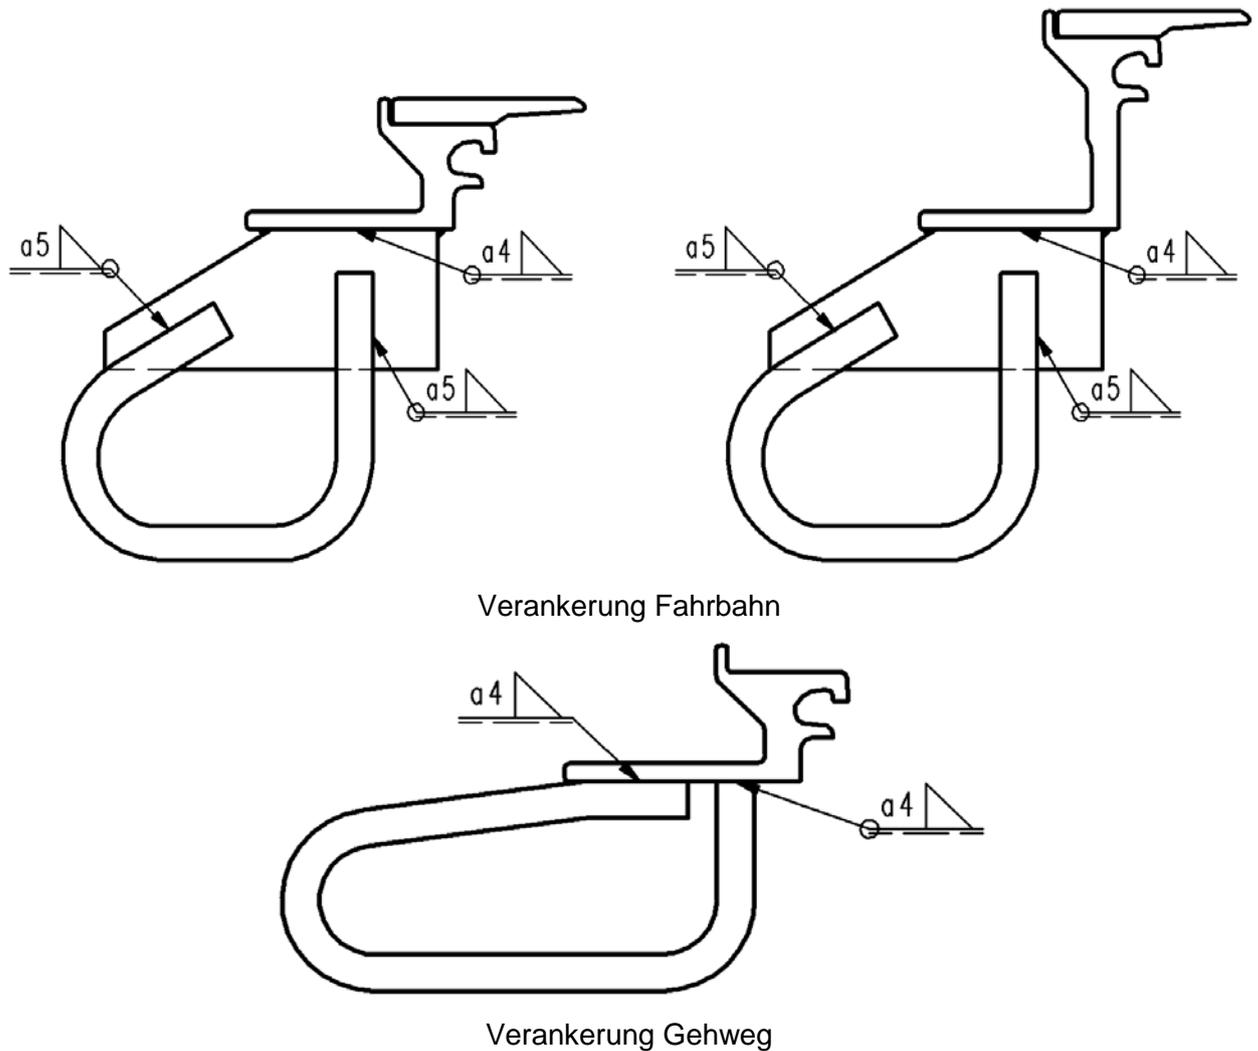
Position und Dimension der Schweißnähte gemäß EN ISO 2553
